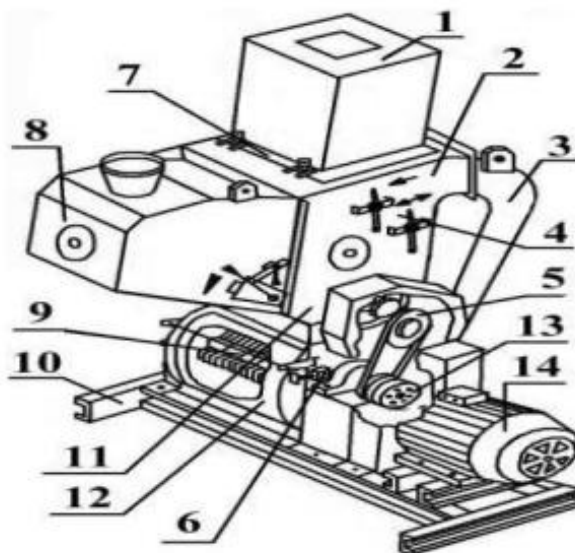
Схема дробарки ДБ-5: 1 – фільтр; 2 – розділювальна камера; 3 – кормопровід; 4 – механізми керування заслінкою; 5 – двохступінчатий шків; 6, 12 – кришка; 7 – рама; 8 – бункер; 9 – ротор; 10 – рама; 11 – корпус; 13 – втулково-пальцева муфта; 14 – електродвигун
